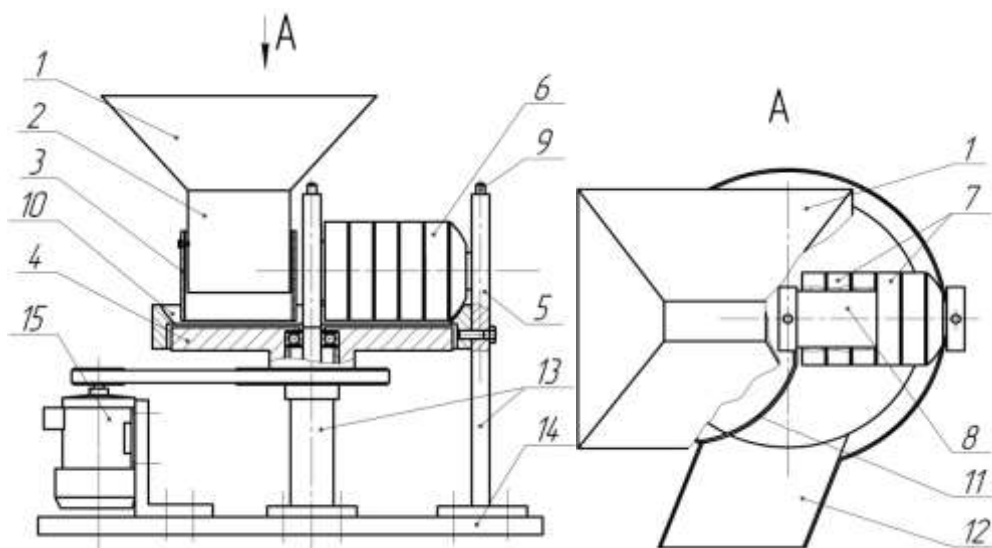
Агрегат для плющения зерна: 1 – бункер; 2 – выгрузная горловина; 3 – дозирующая манжета; 4 – диск; 5 – опора; 6 – валец; 7 – дисковый элемент; 8 – ось; 9 – прижимное устройство; 10 – обечайка; 11 – криволинейный скребок; 12 – выгрузной лоток; 13 – стойка; 14 – рама; 15 – привод
